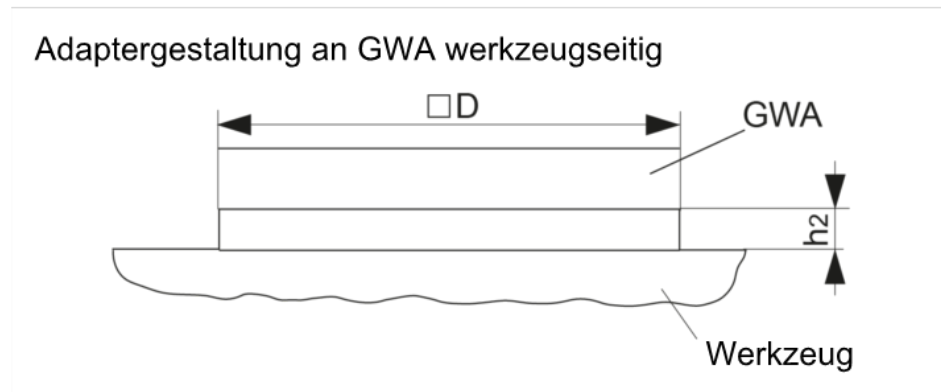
Adaptergestaltung an GWA werkzeugseitig
